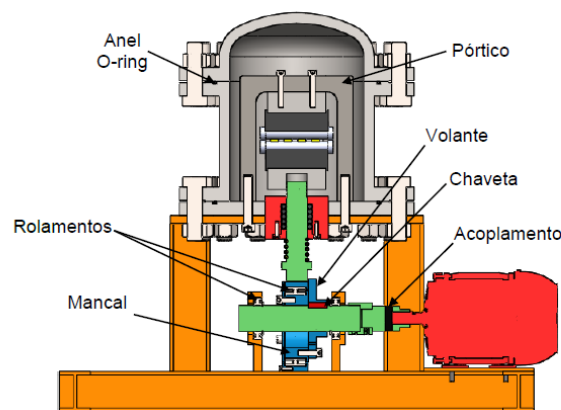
Vista frontal em corte da Máquina de Ensaios de Corrosão-Fadiga com a indicação de componentes
